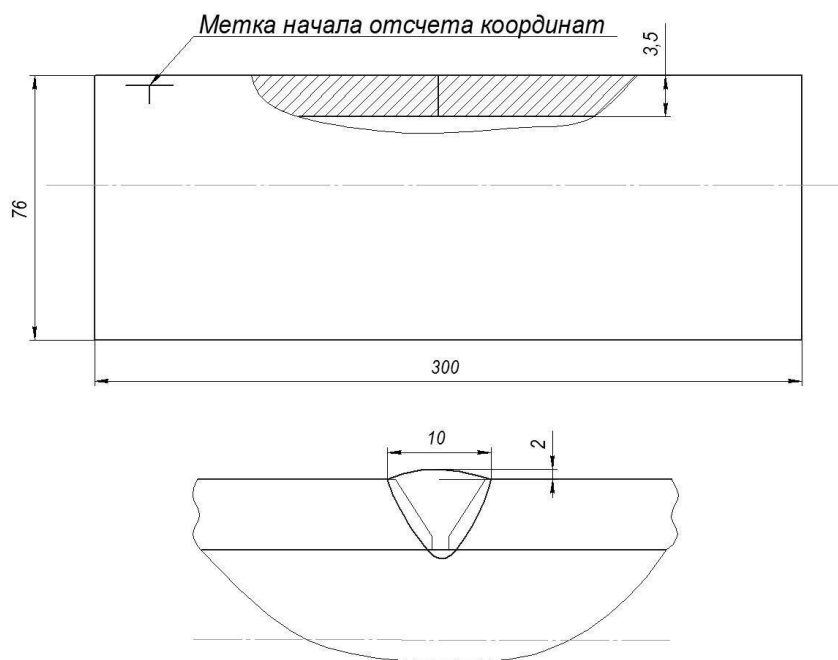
Эскиз сварного соединения и образца
